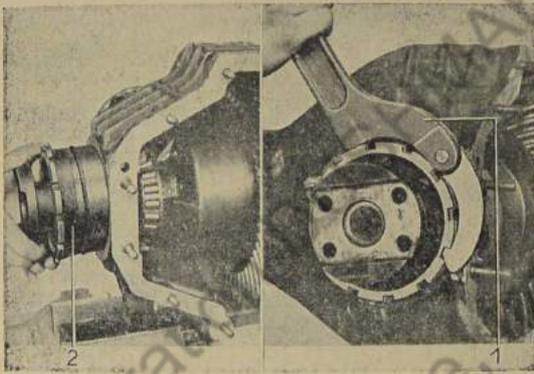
Seitliche Einstellbuchsen heraus-schrauben
